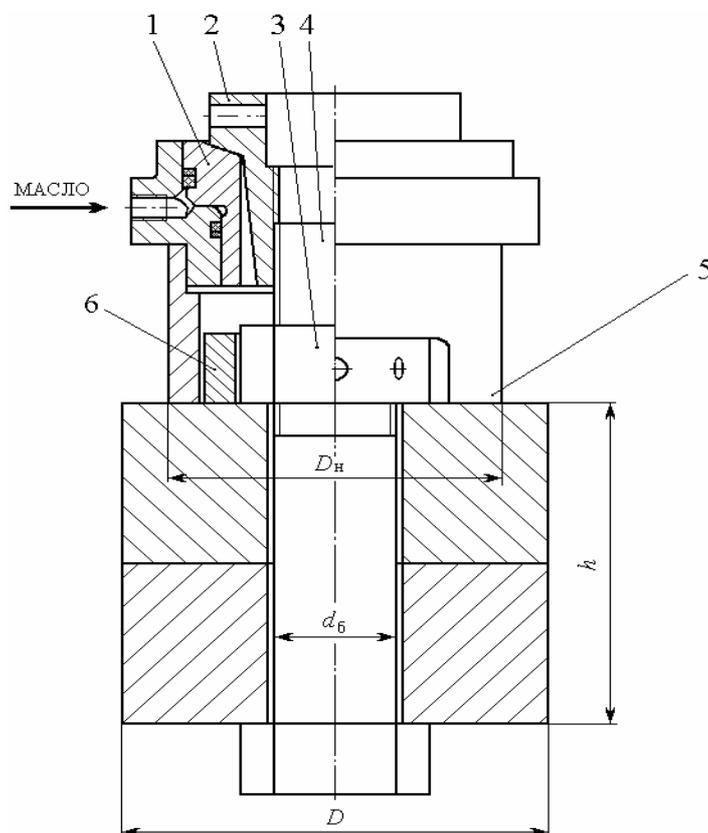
Схема установки гидравлического устройства из серийного ряда
